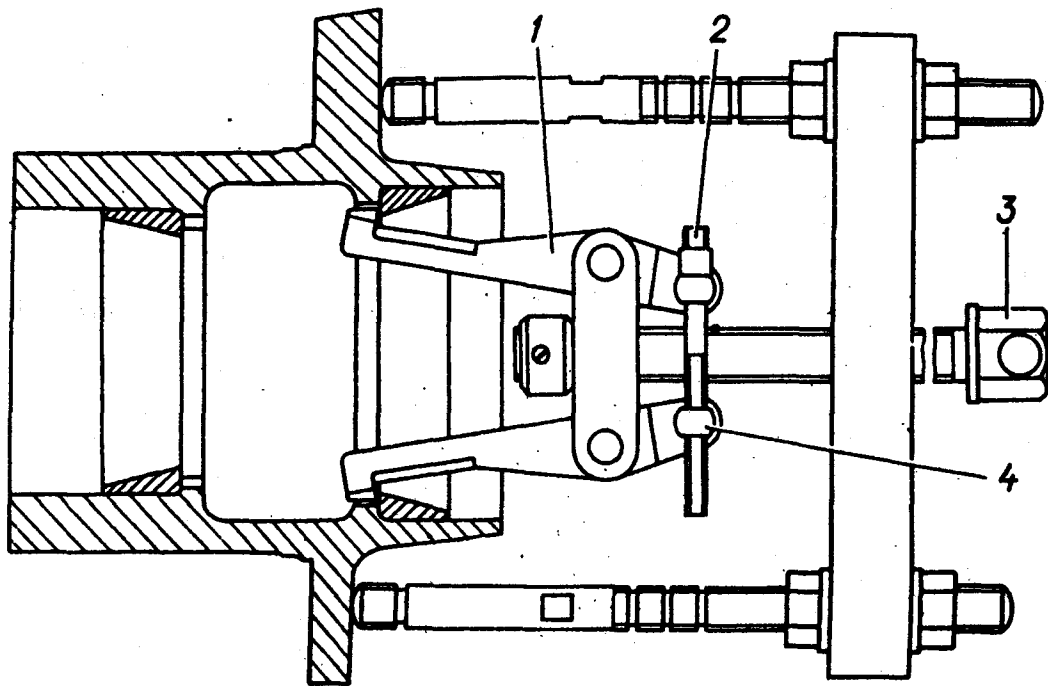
Выпрессовка наружных колец подшипников ступиц колес:
